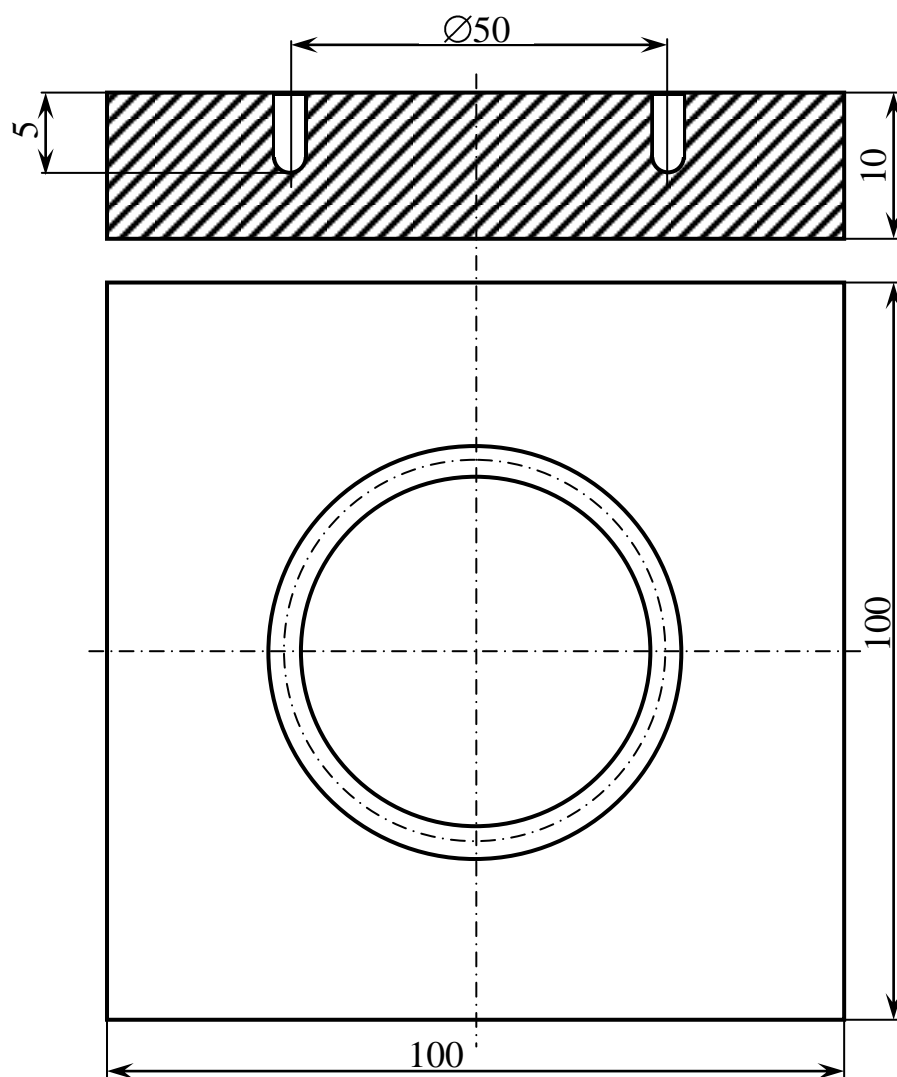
Размеры и форма пробы с кольцевой канавкой
